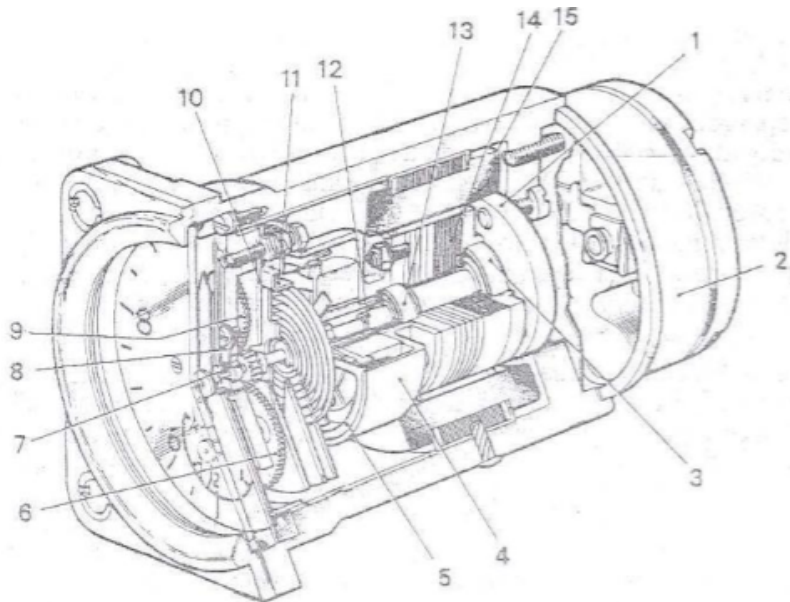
Vista en corte de un indicador de tacómetro típico tipo motor síncrono. 1.—Eje en voladizo. 2.—Conjunto de bloque de terminales. 3.—Cojinete de bolas posterior. 4.—Conjunto de taza magnética. 5.—Conjunto de elemento de resistencia al arrastre. 6.—Husillo y engranaje de la aguja pequeña. 7.—Cojinete exterior del husillo. 8.—Orejeta de bloqueo del cojinete. 9.—Engranaje intermedio. 10.—Placa de apoyo. 11.—Orejeta de sujeción del muelle en espiral. 12.—Cojinete interior del husillo. 13.—Cojinete de bolas delantero. 14.—Rotor. 15.—Estator.
